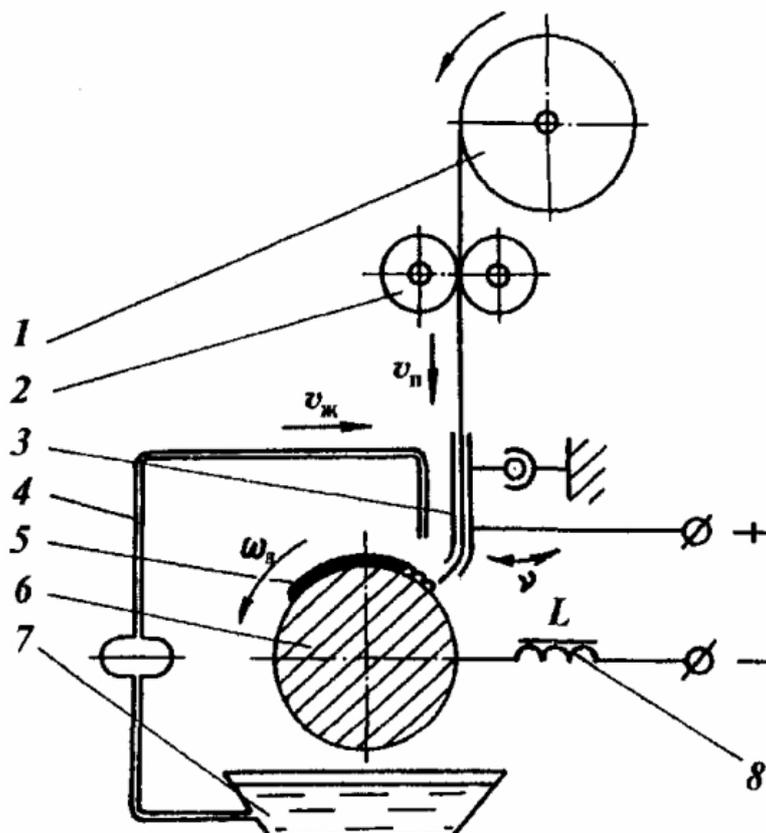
Схема вибродуговой наплавки: 1 – кассета для проволоки; 2 – подающие ролики; 3 – качающийся мундштук; 4 – система подачи раствора; 5 – наплавленный слой; 6 – восстанавливаемая деталь; 7 – емкость; 8 – индуктивное сопротивление; v_p и $v_{ж}$ – скорость подачи соответственно проволоки и раствора; ω_d – угловая частота вращения детали; ν – частота качаний мундштука; L – индуктивность
